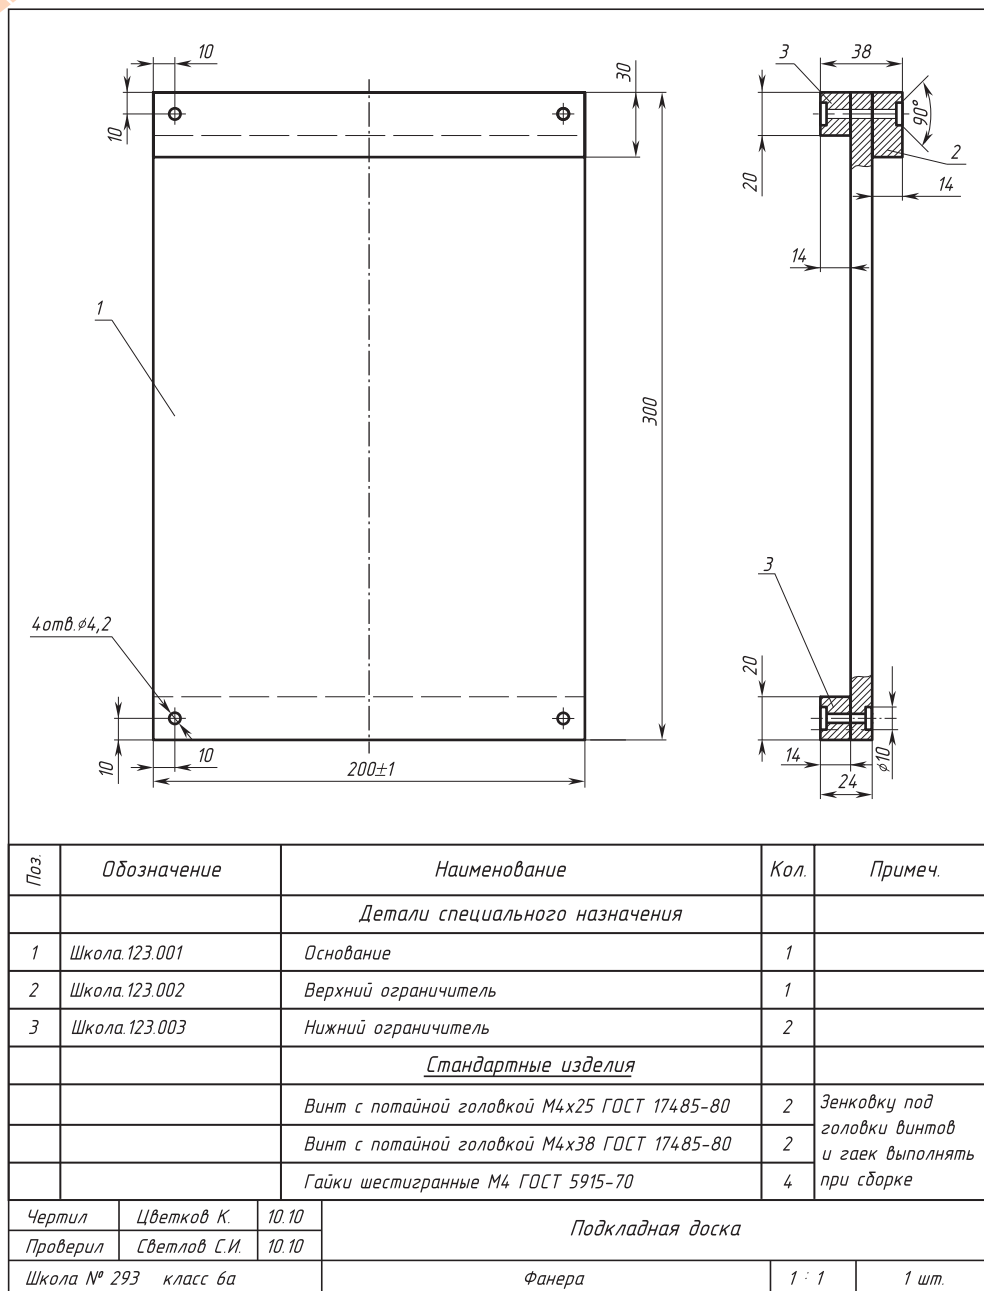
Сборочный чертёж подкладной доски для столярного верстака
